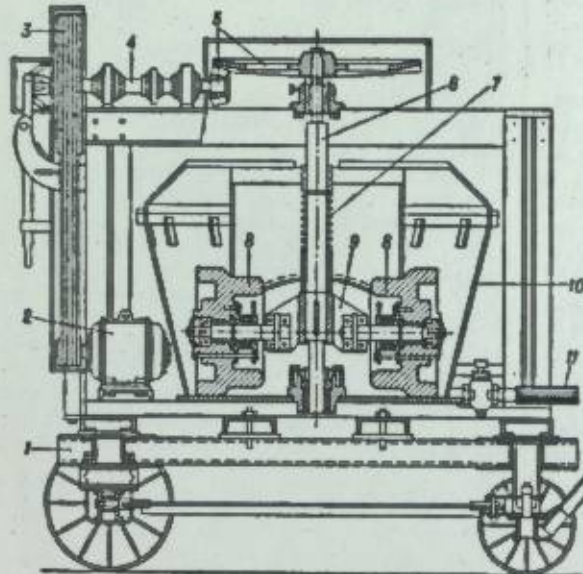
Известегасильная машина ЮЗ бегункового типа: 1 — ходовая рама; 2 — электродвигатель; 3 — клиноременная передача; 4 — главный вал; 5 — коническая передача; 6 — вертикальный вал; 7 — шруинка; 8 — бегуны; 9 — траверса; 10 — сильный сосуд; 11 — сливной трубопровод.
